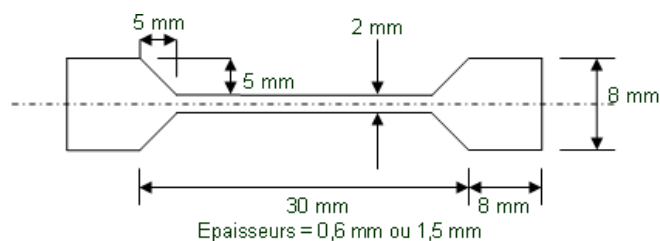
Schéma et dimensions des éprouvettes de traction
